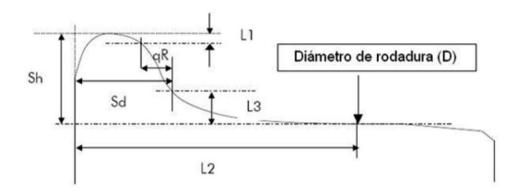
Parámetros de Rodadura Fuente: SE-01-ES-IT.302.T2.01 Instrucción Técnica Reperfilado de ALSTOM [1]
